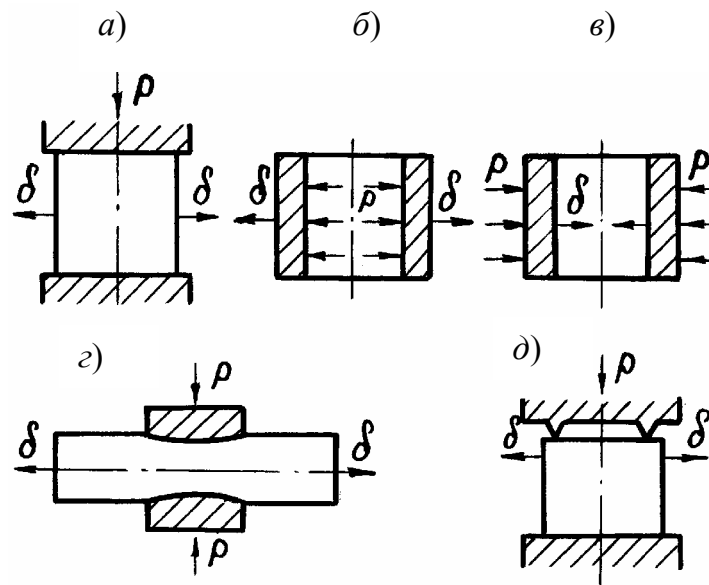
Схемы процессов для восстановления размеров деталей: а – осадка; б – раздача; в – обжатие; г – вытяжка; д – вдавливание
